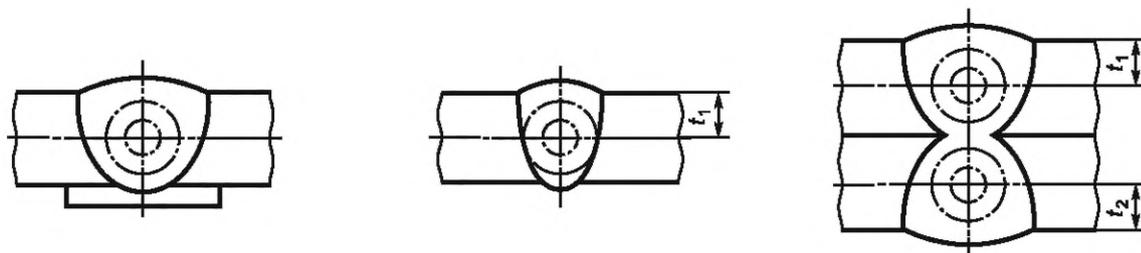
Пример расположения образцов для испытаний. Продольный плоский разрез
